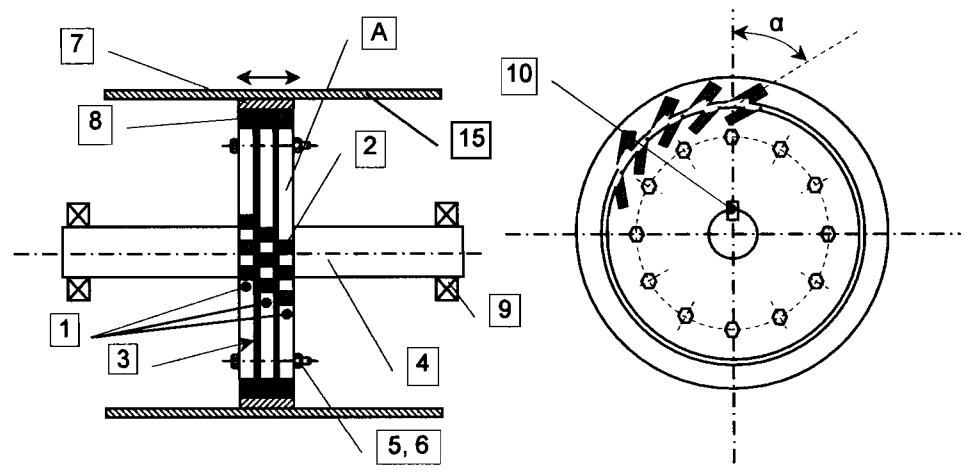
Motor magnetic cu ax orizontal și pornire/oprire axială, cu un grup rotoric
